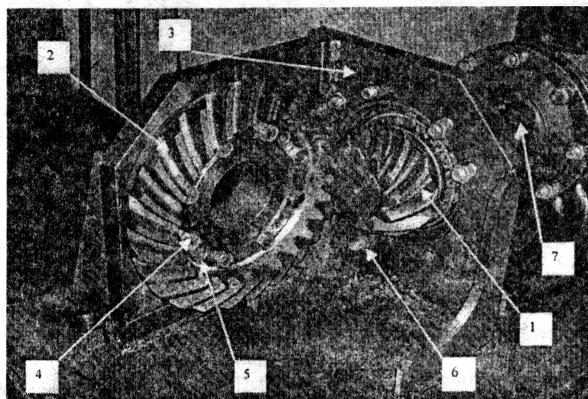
Испытания чугунных шестерен главной пары автомобиля МАЗ-5551: 1 – ведущая шестерня; 2 – ведомая шестерня; 3 – стойка; 4 – болты крепления ведомой шестерни; 5 – штифты; 6 – болты крепления стакана подшипников; 7 – стакан подшипников
